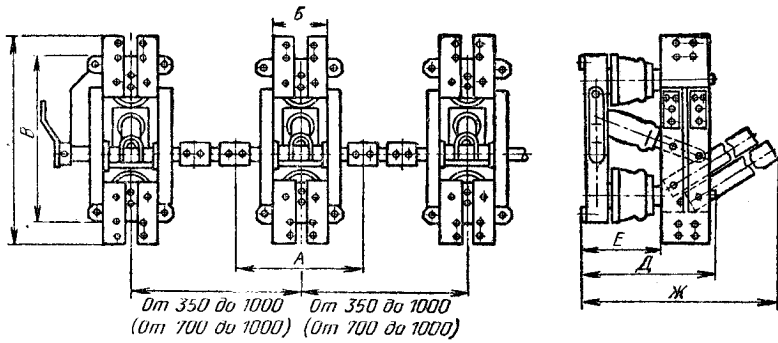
Разъединитель РВК-10 (в скобках размеры для разъединителя РВК-20).
